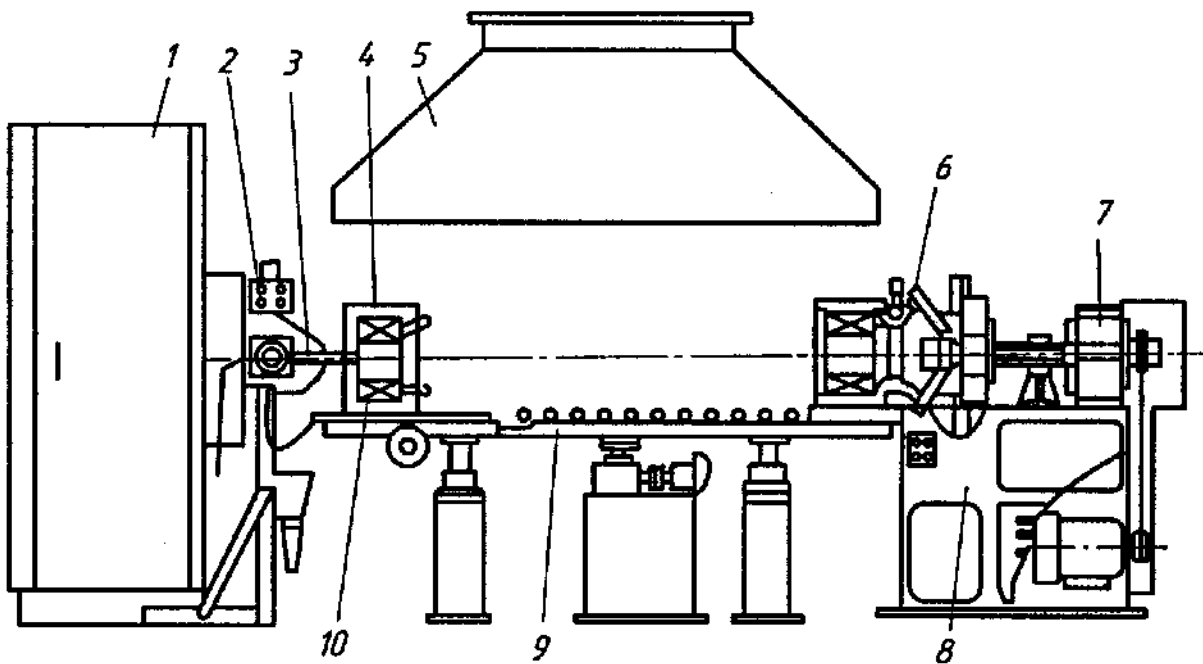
Схема высокочастотной установки для разогрева и извлечения обмотки статора: 1 – генератор; 2 – пульт управления; 3 – зажим; 4 – статор; 5 – вытяжной зонт; 6 – крючки; 7 – пневматический цилиндр; 8 – механизм выдергивания; 9 – рольганг; 10 – индуктор
